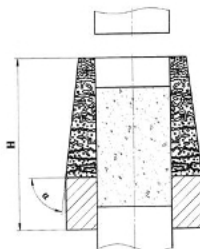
Пресс-форма для прессования блоков электрощеток
